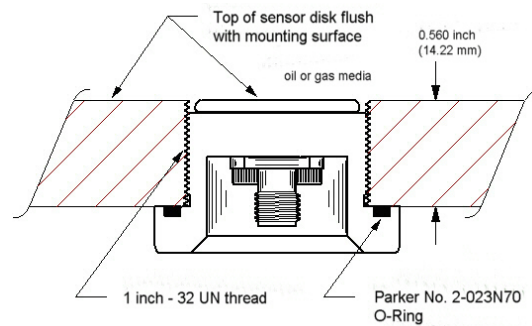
Montage d'une sonde SIE-100 à travers la paroi d'un guide. (Source VOSS Scientific LLC)
